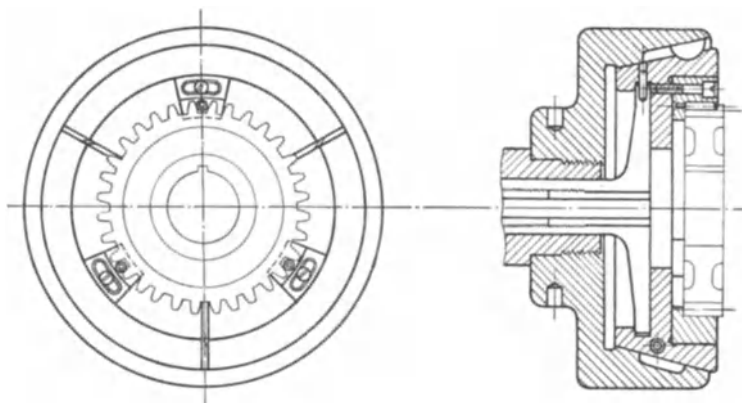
Spannfutter zum Schleifen für gehärtete Zahnräder.
